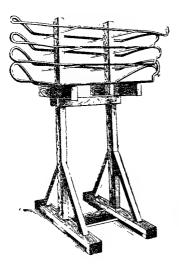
Станок-этажерка для ручиой изолировки витков секций.
